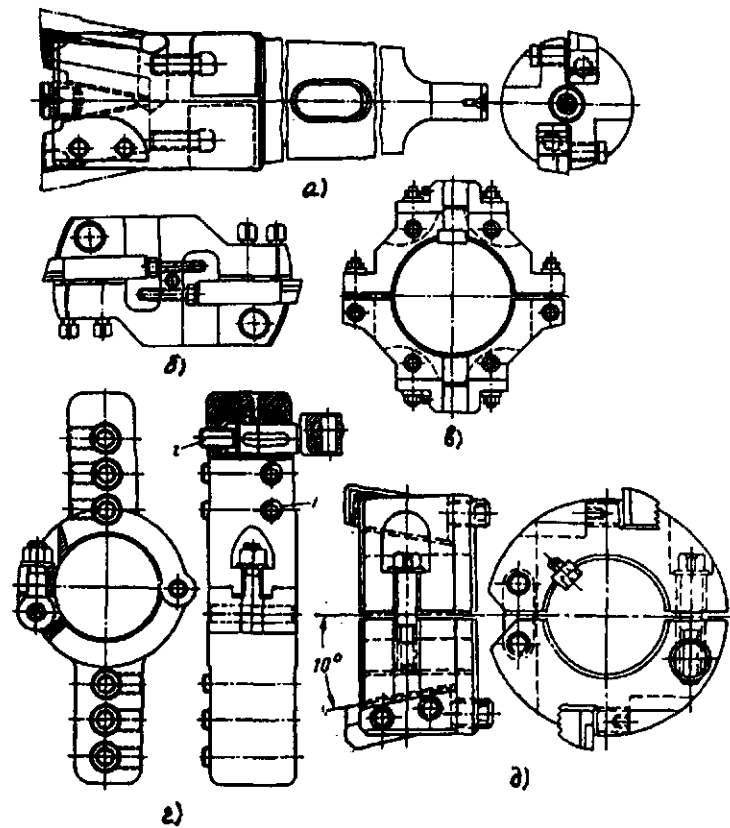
Расточные головки: а – двухрезцовая концевая; б – насадная; в – разъемная; з – для упоров, применяемая при подрезке торцов и расточке выточек; д – разъемная расточная с двумя резцами для установки на борштанге
